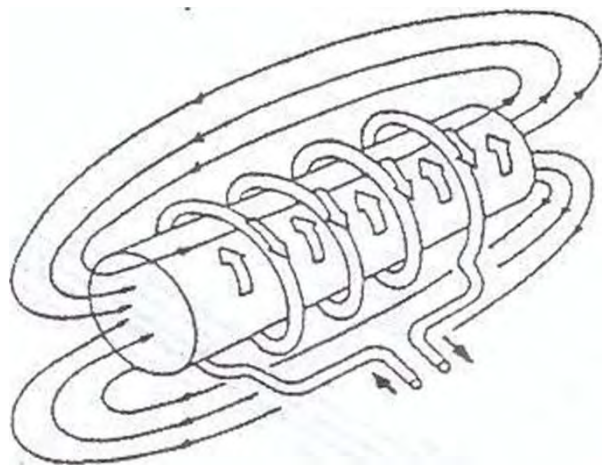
Принцип индукционного нагрева поверхностного слоя заготовок.
